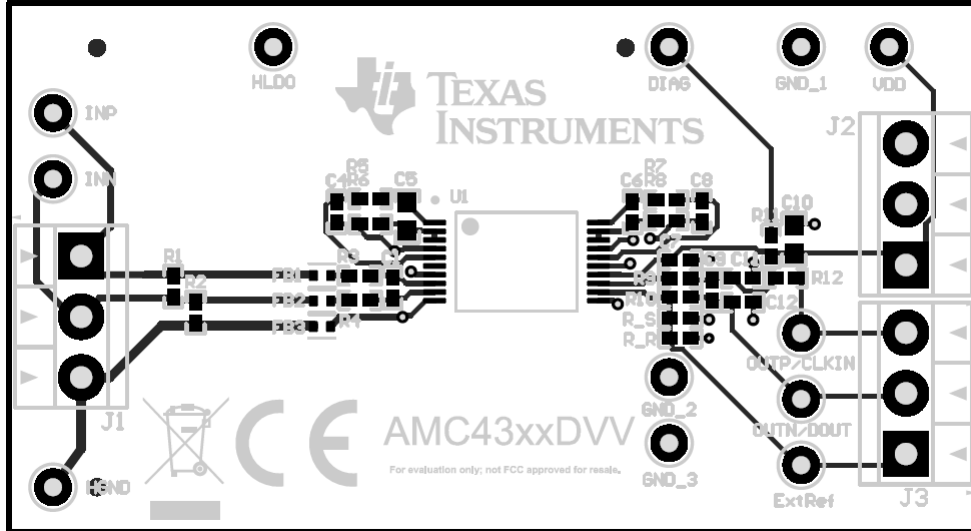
AMC43xxDVVEVM 顶部 PCB 图
